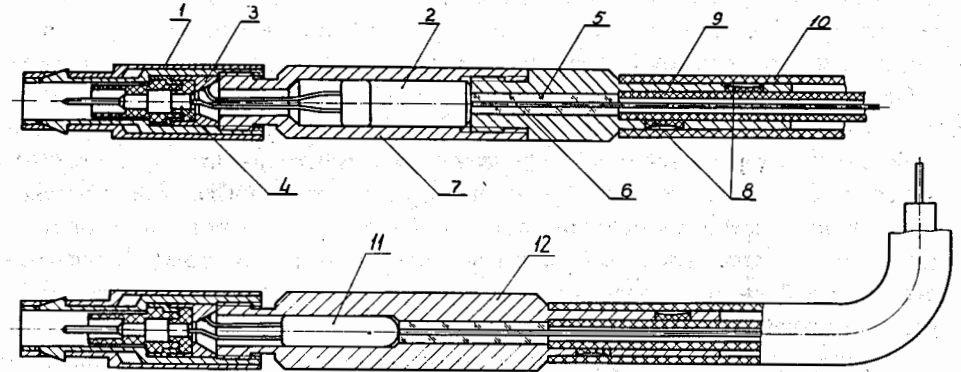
Активный разъемный соединитель с использованием электрического разъема типа LEMO: (1 — корпус; 2 — фотодиод; 3-4 — точки распайки электрических выводов; 5 — капилляр; 6-12 — наконечники; 7 — корпус приборной части; 8 — отверстия в хвостовике для нанесения клея; 9 — ВОК; 10 — защитный кембрик; 11 — светодиод).
